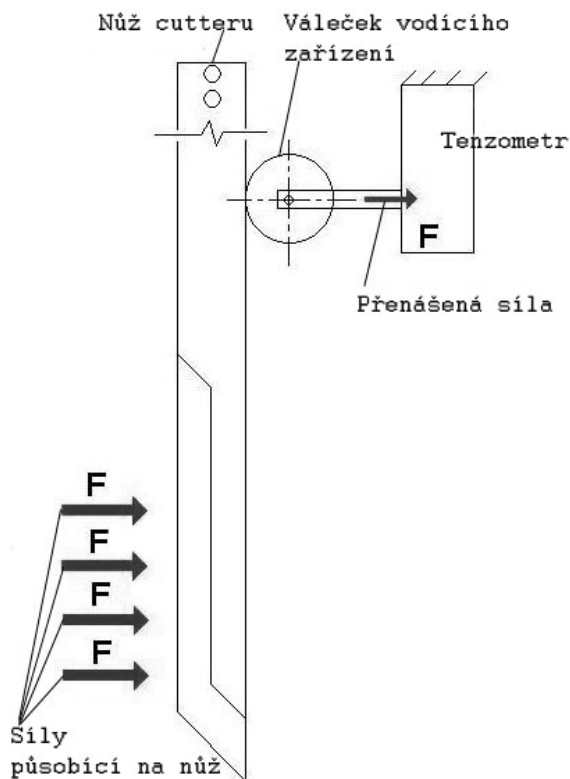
Detail vodícího zařízení nože cutteru MX9 [12]
